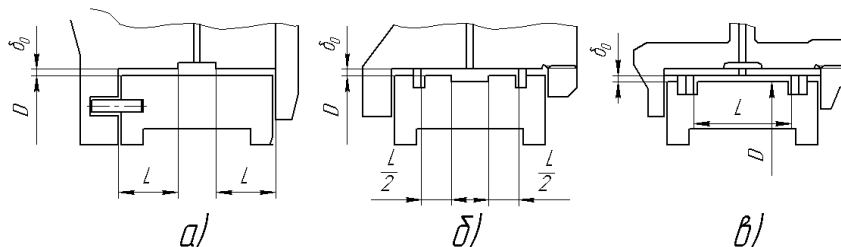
Конструктивные типы ГДД: а – короткий проточный; б – короткий непроточный; в – длинный
